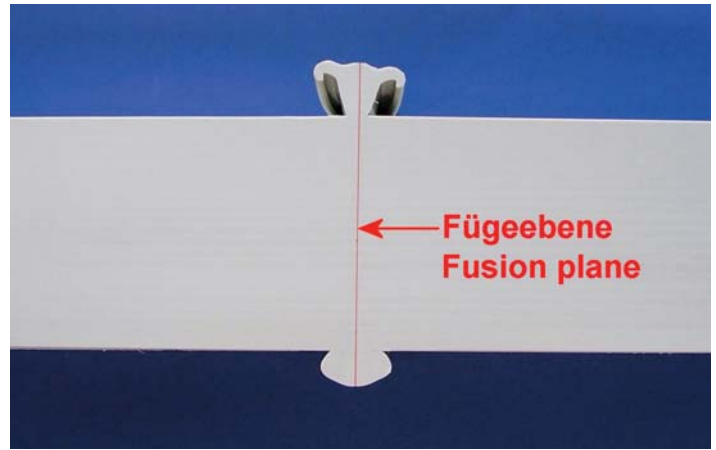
Fügeebene eines geschweißten Probekörpers aus einem PP-R Hohlstab mit 100 mm Wanddicke
